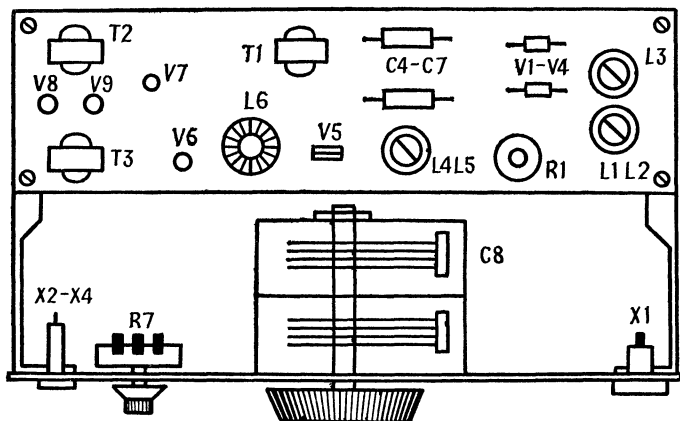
Конструкция и расположение деталей приемника на 160 м
